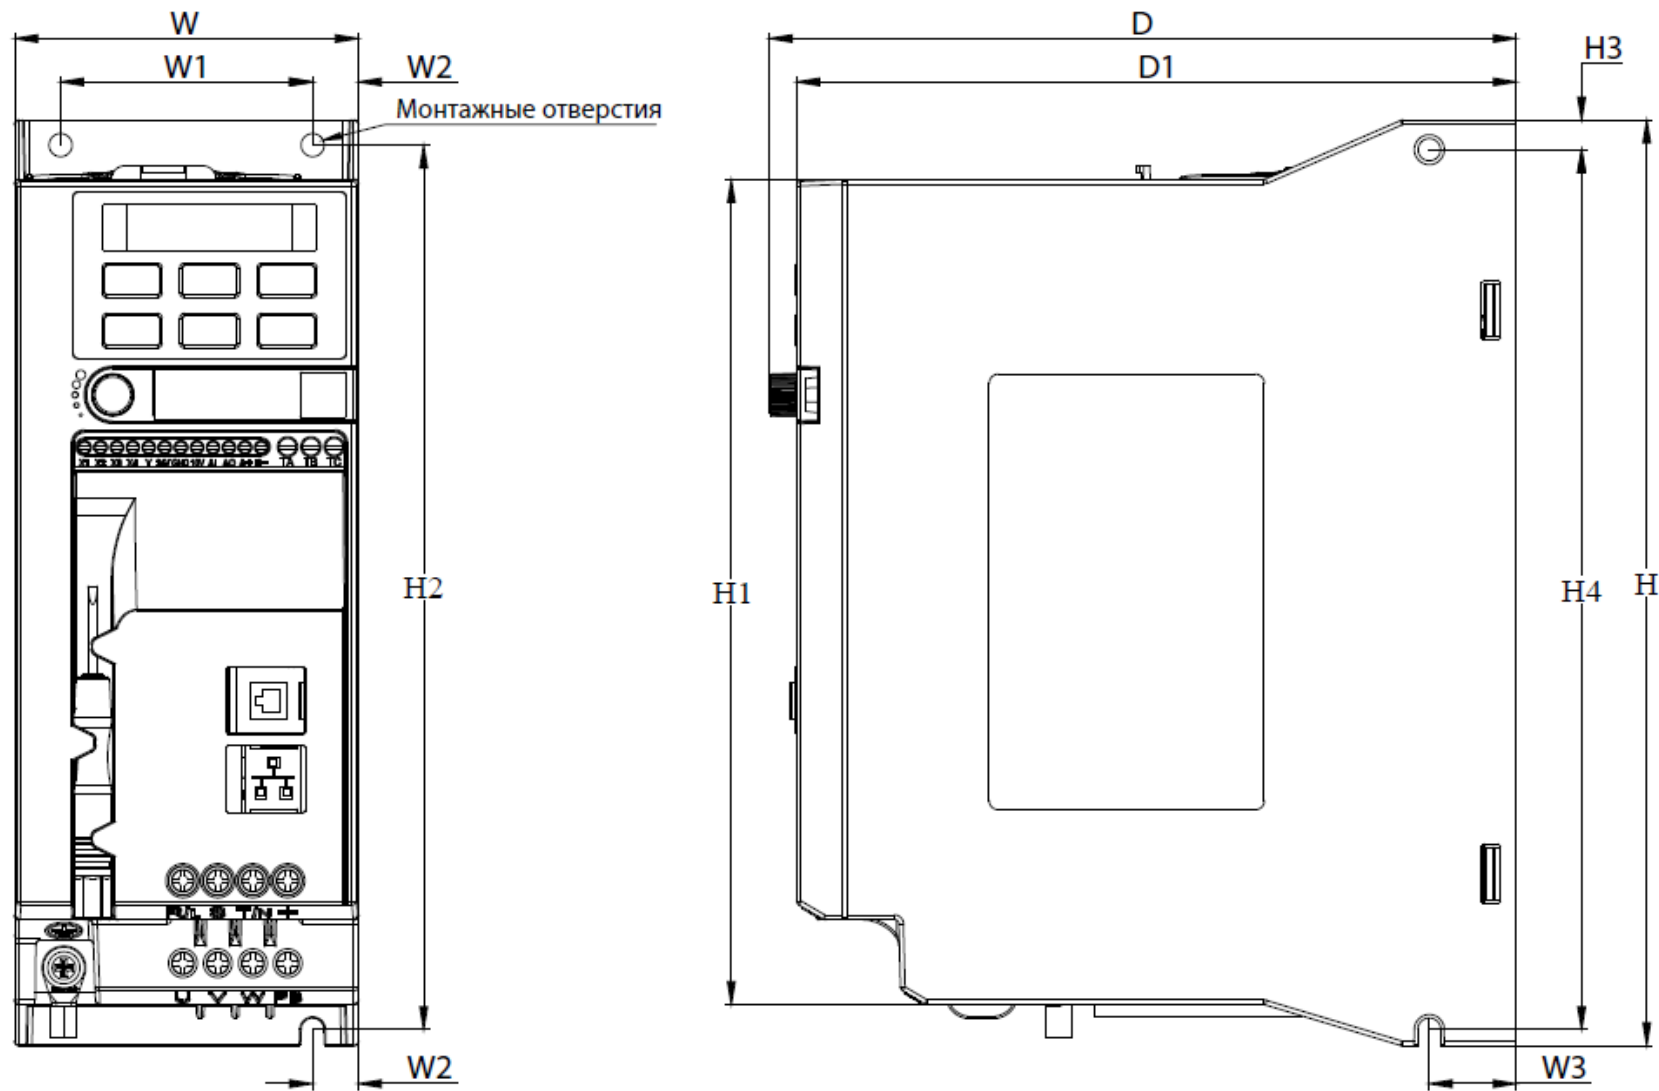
Чертеж преобразователя частоты типоразмер A2
